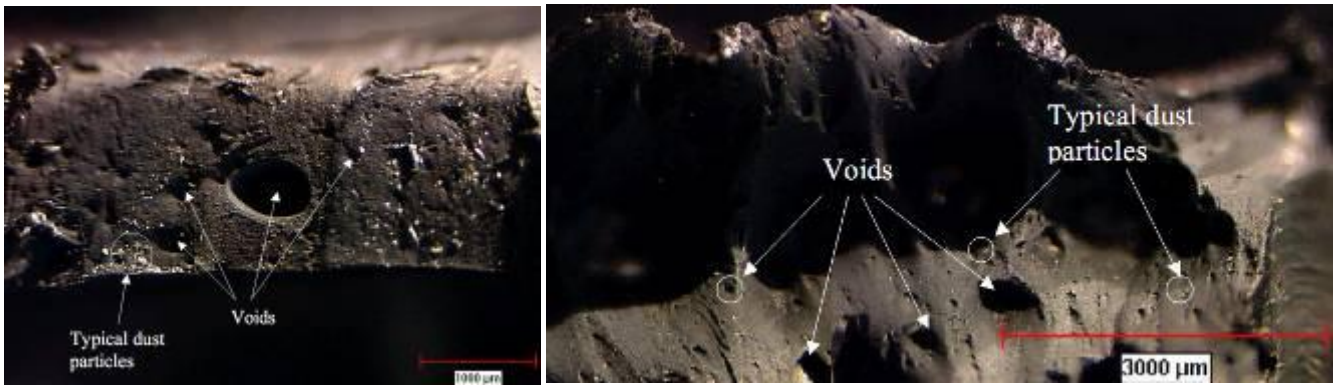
Presencia de partículas en la soldadura [22].
